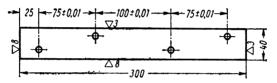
Деталь с длинной и короткой базовыми боковыми сторонами
